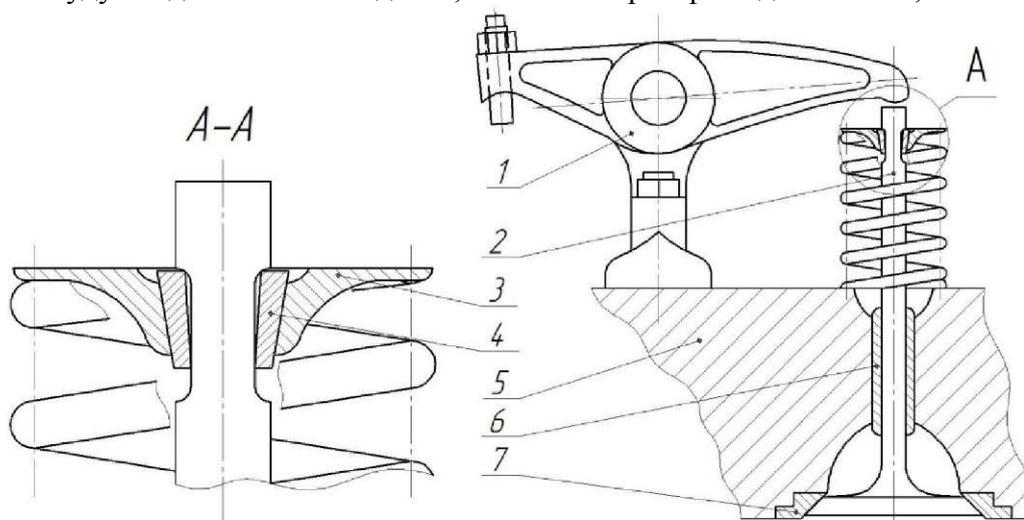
Крепление клапана 1 - Клапанный рычаг (коромысло); 2 - Клапан; 3 - Упорная тарелка; 4 - Сухари; 5 - Крышка цилиндра; 6 - Направляющая втулка; 7 - Клапанное гнездо
